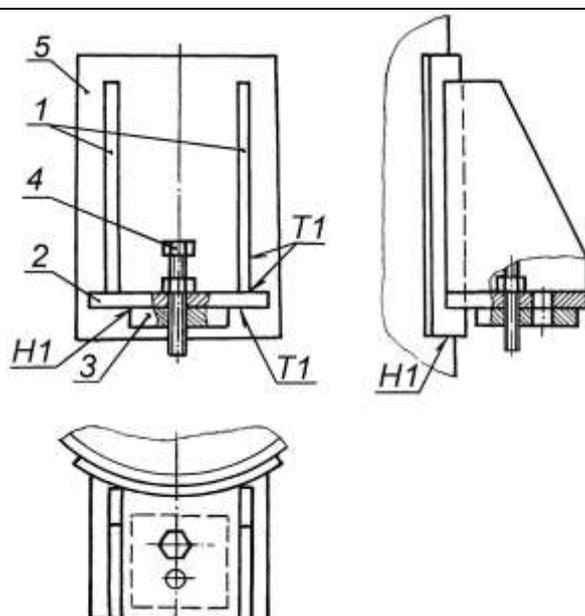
Сварная опорная лапа (тип 2) для вертикальных теплообменников: 1 – косынка; 2 – основание; 3 – подкладной лист; 4 – регулировочный болт с контргайкой; 5 – накладной лист
